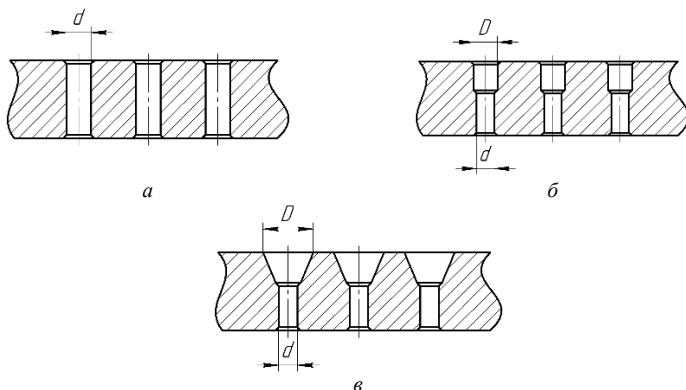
Схема исполнения фильер матрицы пресс-грануляторов: а – фильера без рассверловки; б – фильера с цилиндрической рассверловкой; в – фильера с конической рассверловкой; d – диаметр фильеры; D – диаметр рассверловки
